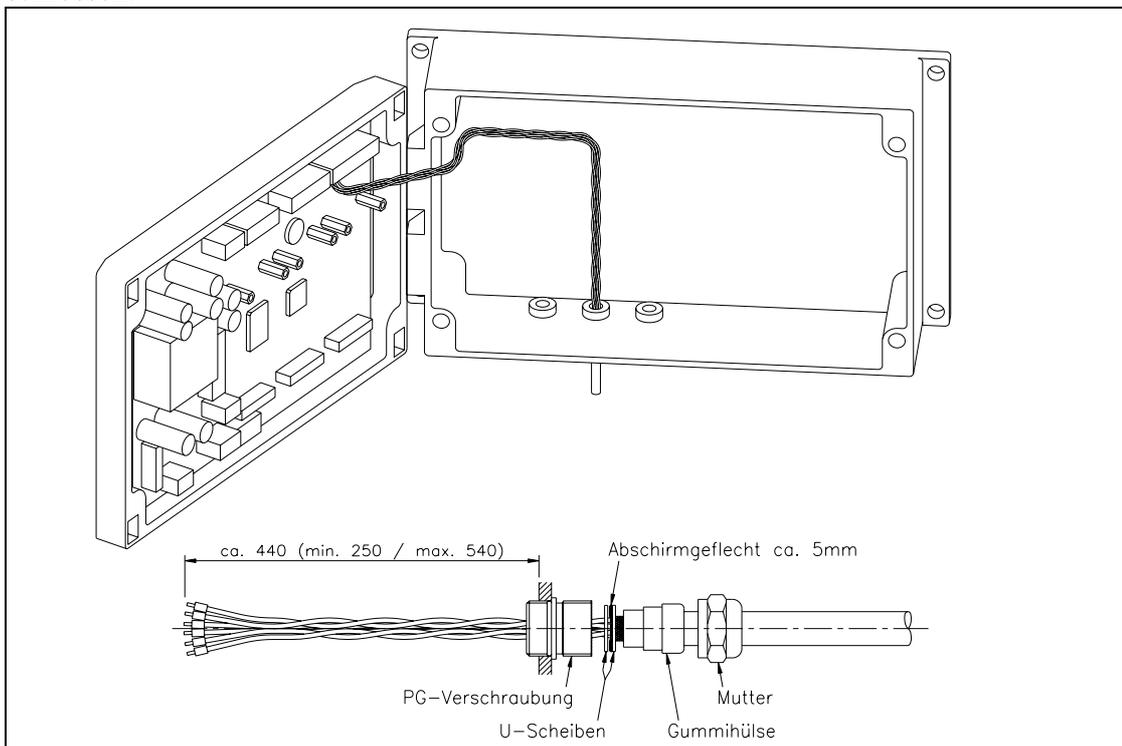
Verlauf der Anschlusskabel im Gehäuse
